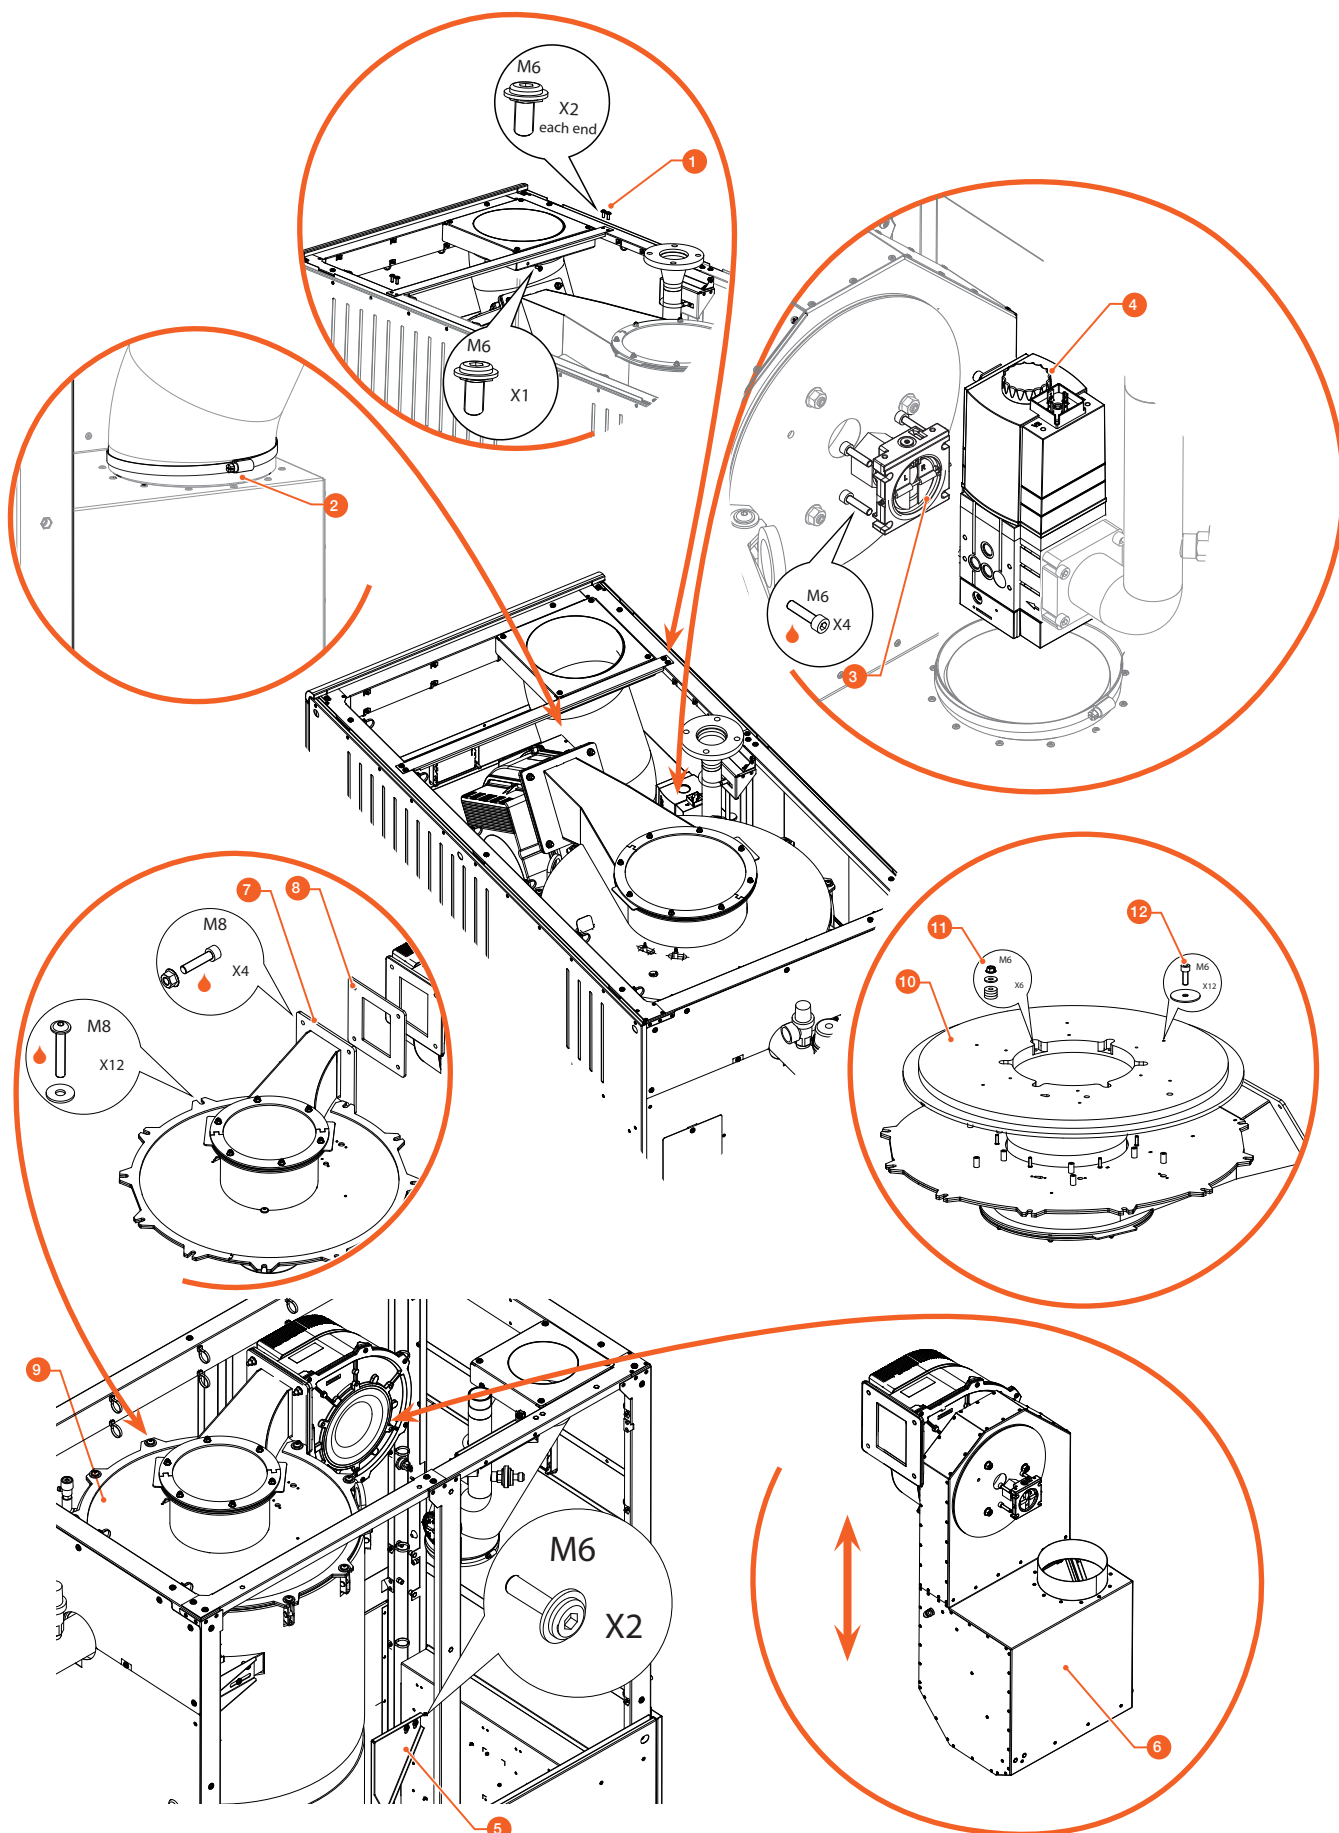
Sostituzione isolamento piastra bruciatore (NESTA PLUS 420 to 840)
